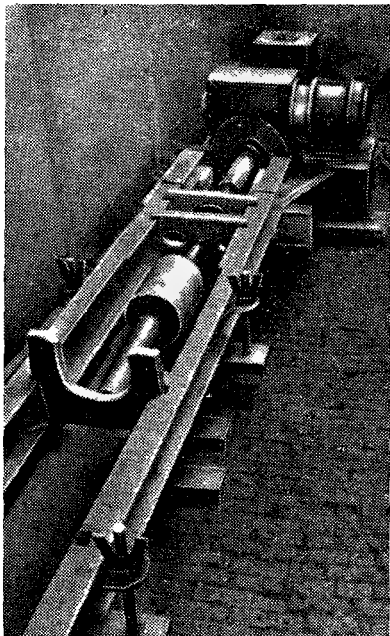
Приспособление для выпрессовки и запрессовки валов у электродвигателей мощностью до 25 квт
